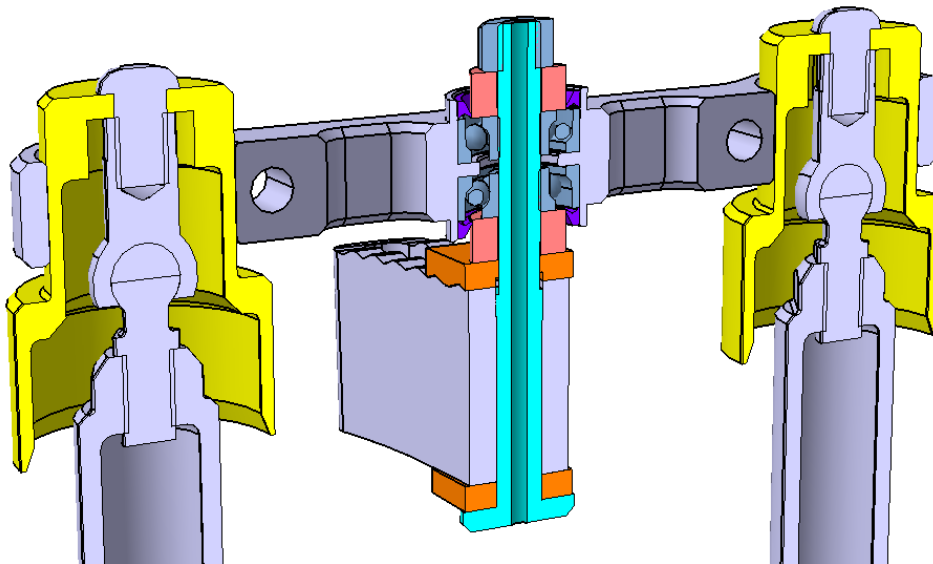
Corte de los conjuntos MT2-DI-01-00 y MT2-DI-00-00 instalados sobre la motocicleta.
